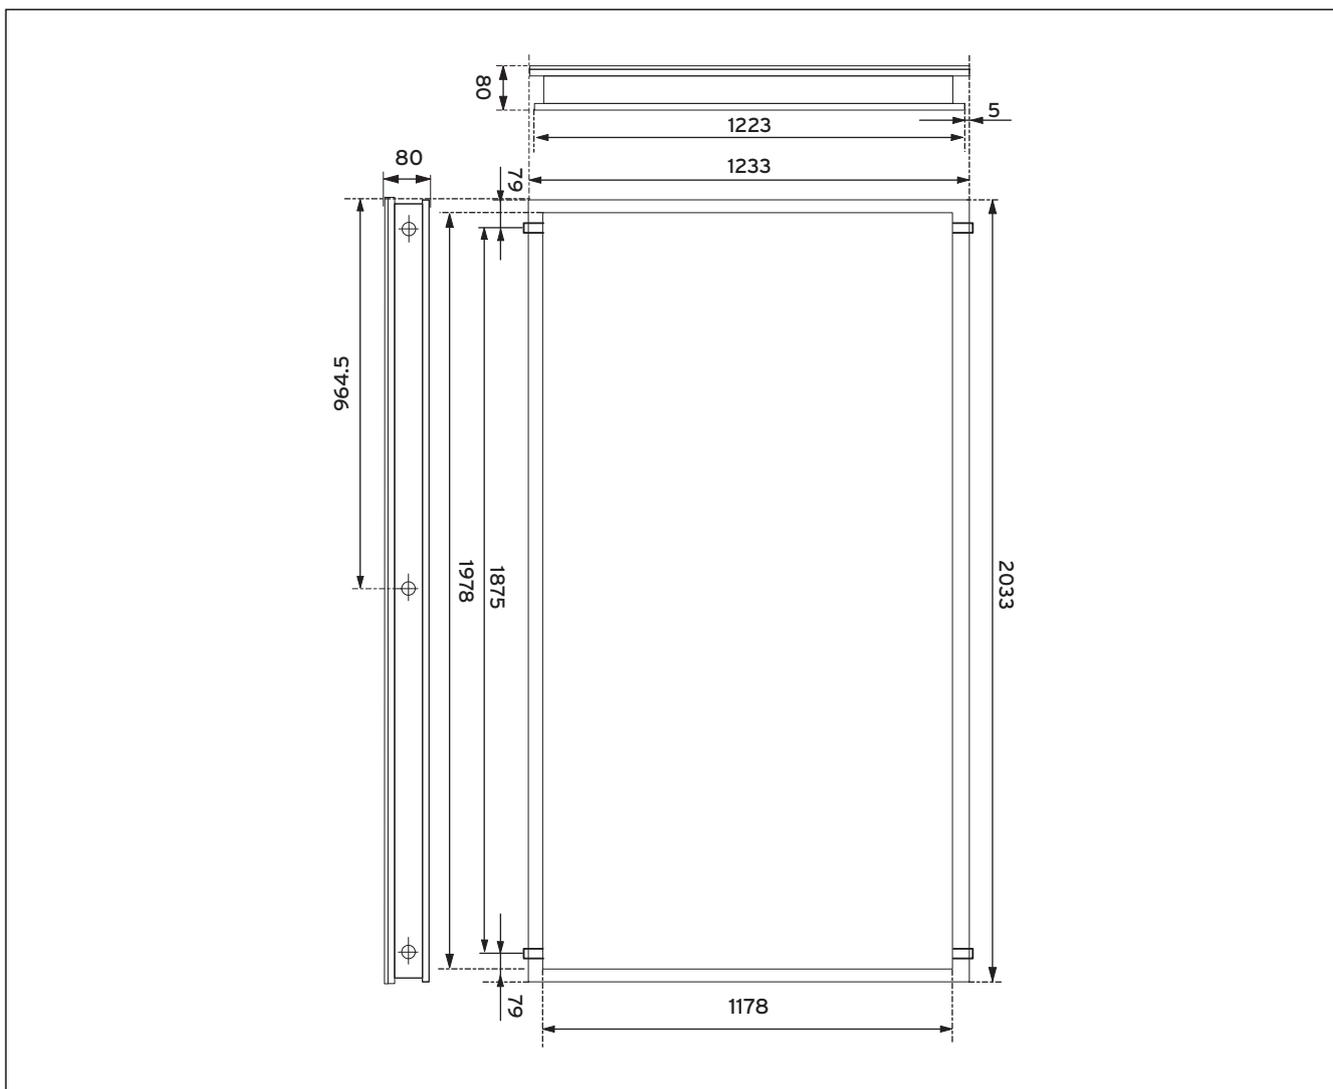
Размерный чертеж VFK 135/2 VD
